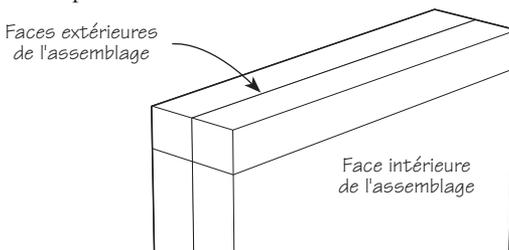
Les planches sont soigneusement alignées, face contre face, pour le traçage.
